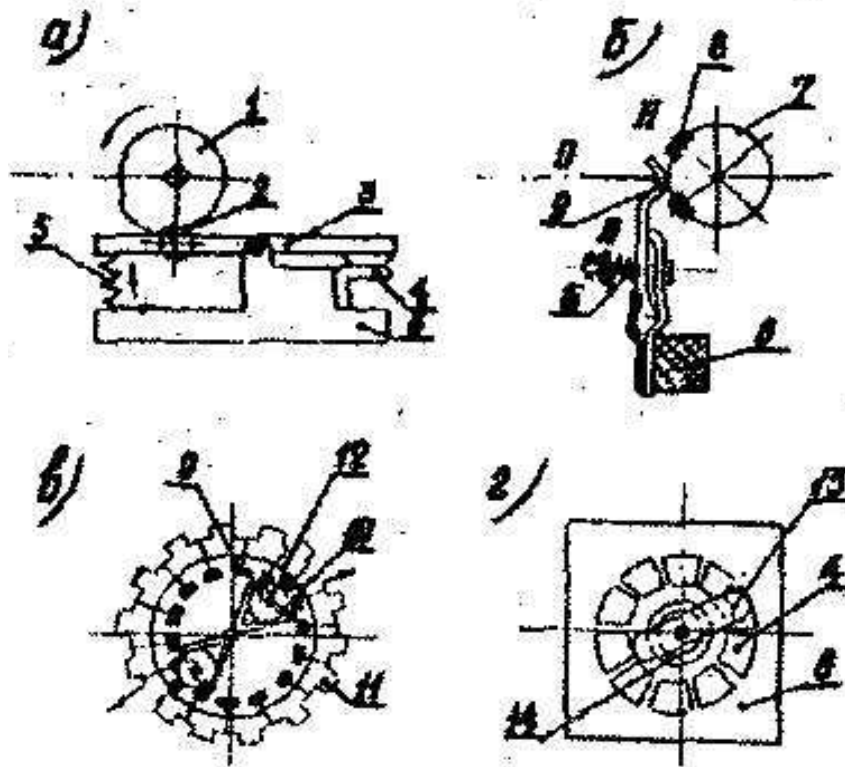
Конструктивне виконання контролерів: а – кулачкові; б – барабанні; в – клавішні; г – реостатні; 1 – шайба кулачкова; 2 – ролик; 3 – важіль; 4 – контакта; 5 – пружина, що притискує; 6 – основа; 7 – барабан; 8 – сегменти; 9 – контактний палець; 10 – струмопровідне кільце; 11 – резистори; 12 – ролик, що притискує; 13 – повзун; 14 – кільце, що знімає струм.
